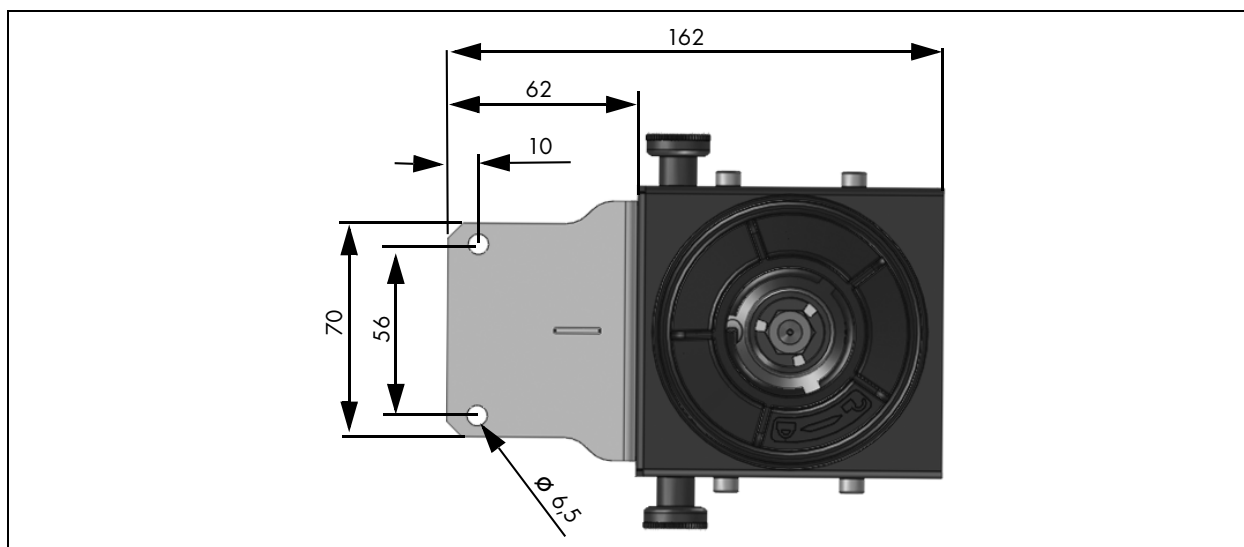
Dimensiones de montaje de la escuadra de fijación
